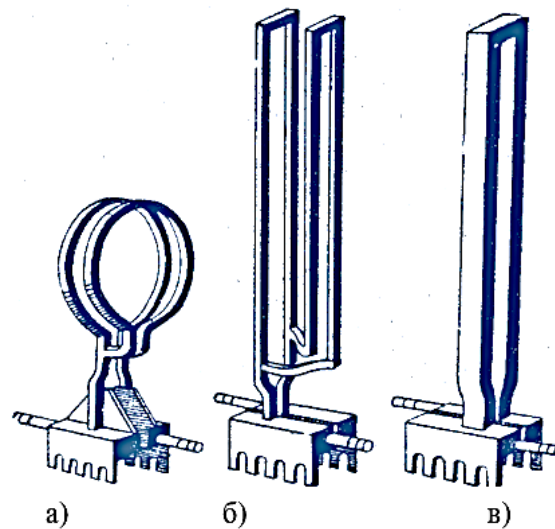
Індуктори для паяння твердосплавних дискових фрез [51, 52]:
